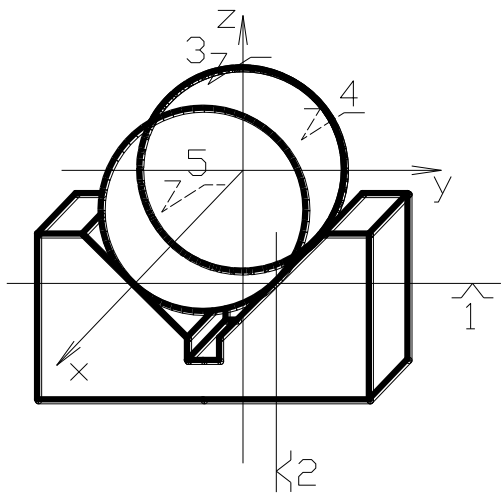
Базування по короткій зовнішній поверхні обертання
